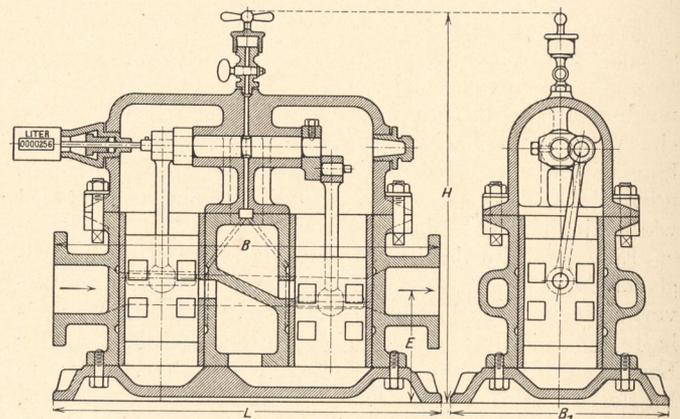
Doppelkolbenwassermesser System Schmid. Ausführung: Emil Kegler, Düsseldorf-Eller.
